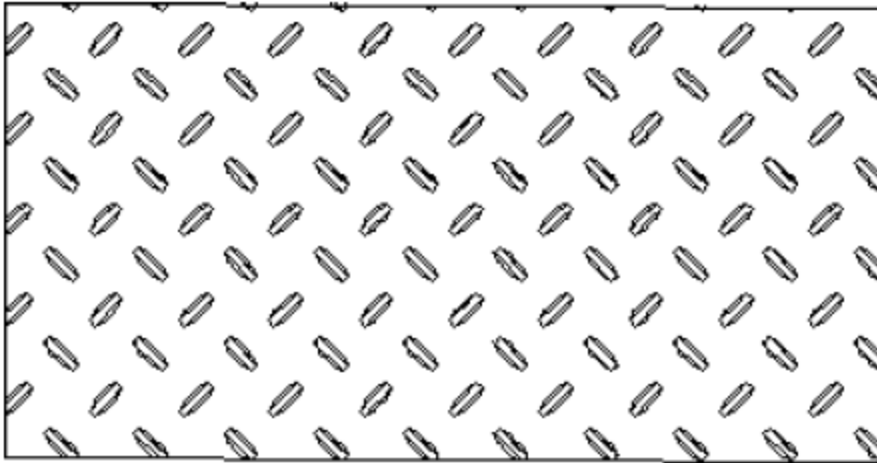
Detalle del dibujo de la plancha de acero.
